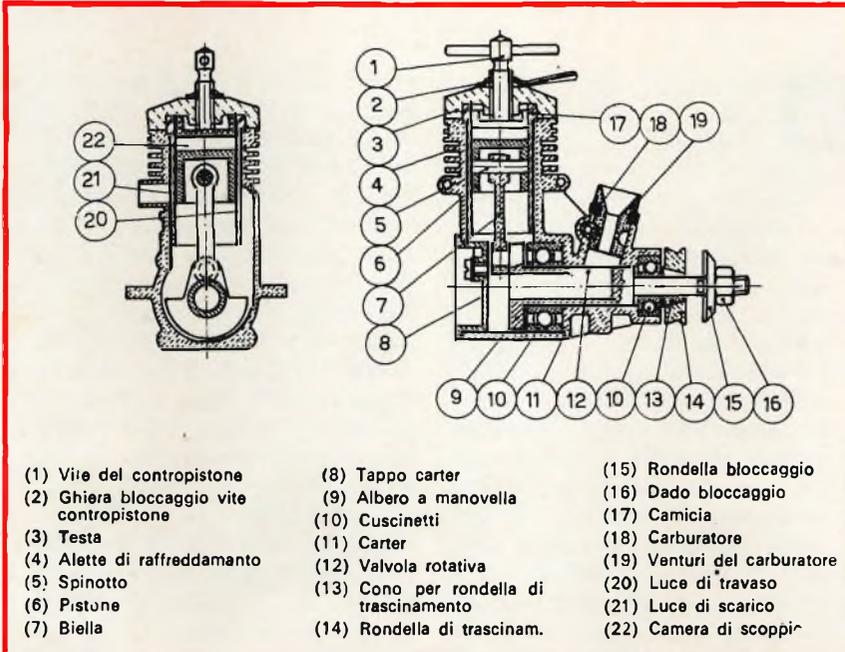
Disegno illustrante tutte le parti meccaniche che compongono un motore diesel.
